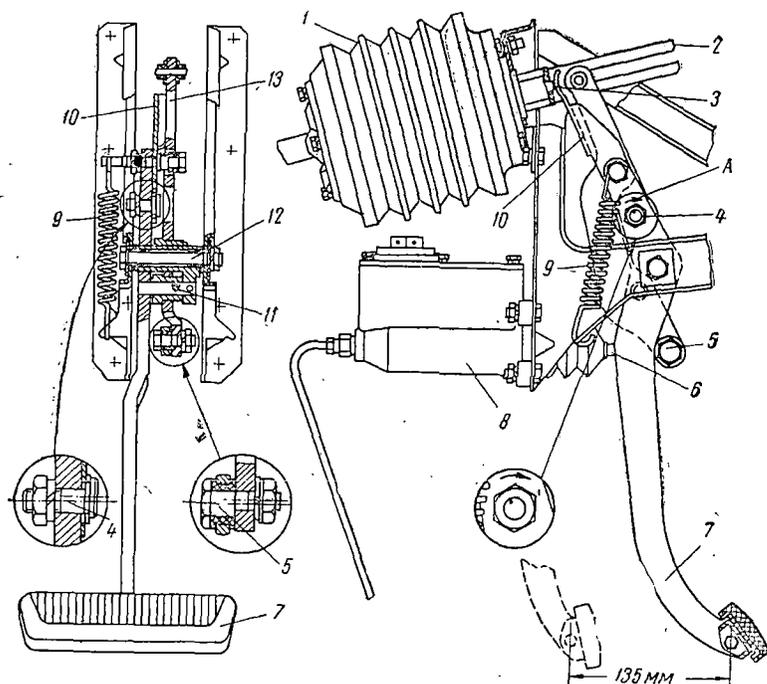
Вакуумный усилитель гидравлического привода тормозов автомобиля ГАЗ-13 «Чайка»:
